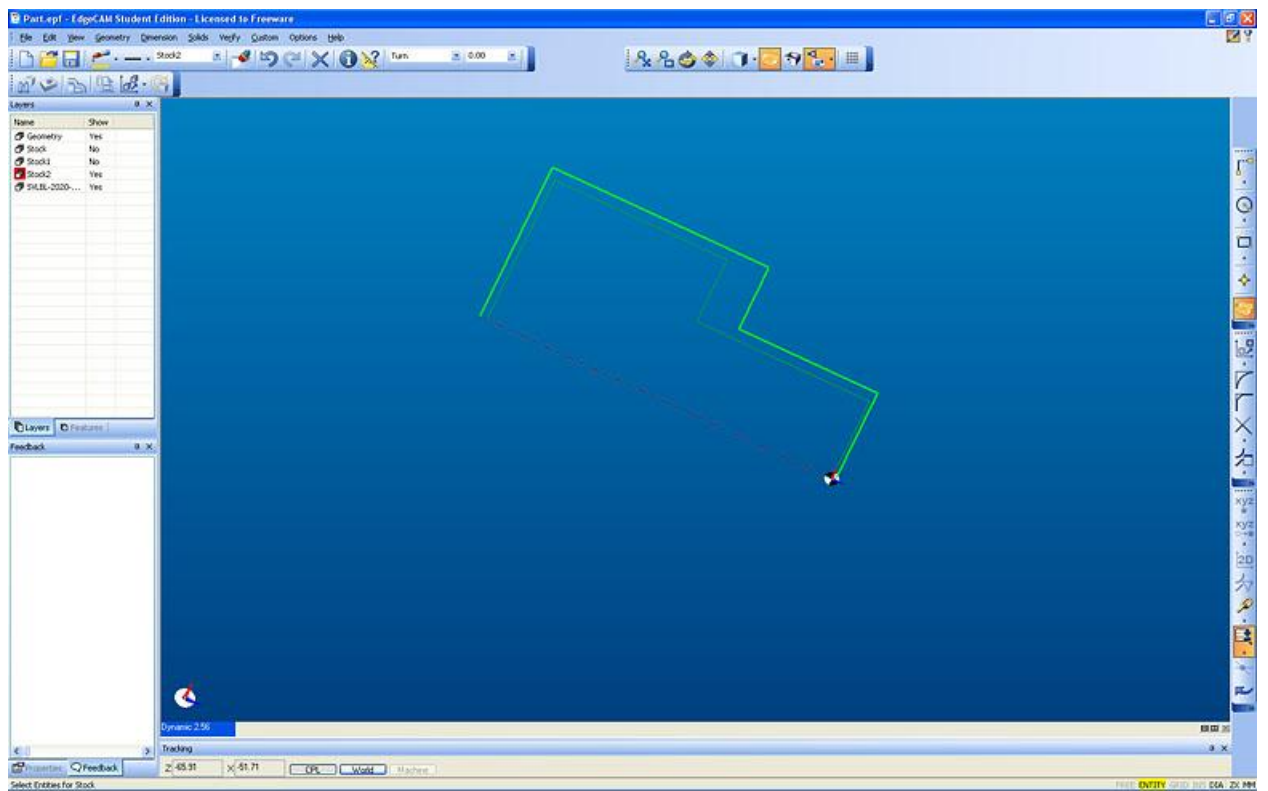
Edgecam. Создание заготовки для токарной обработки
